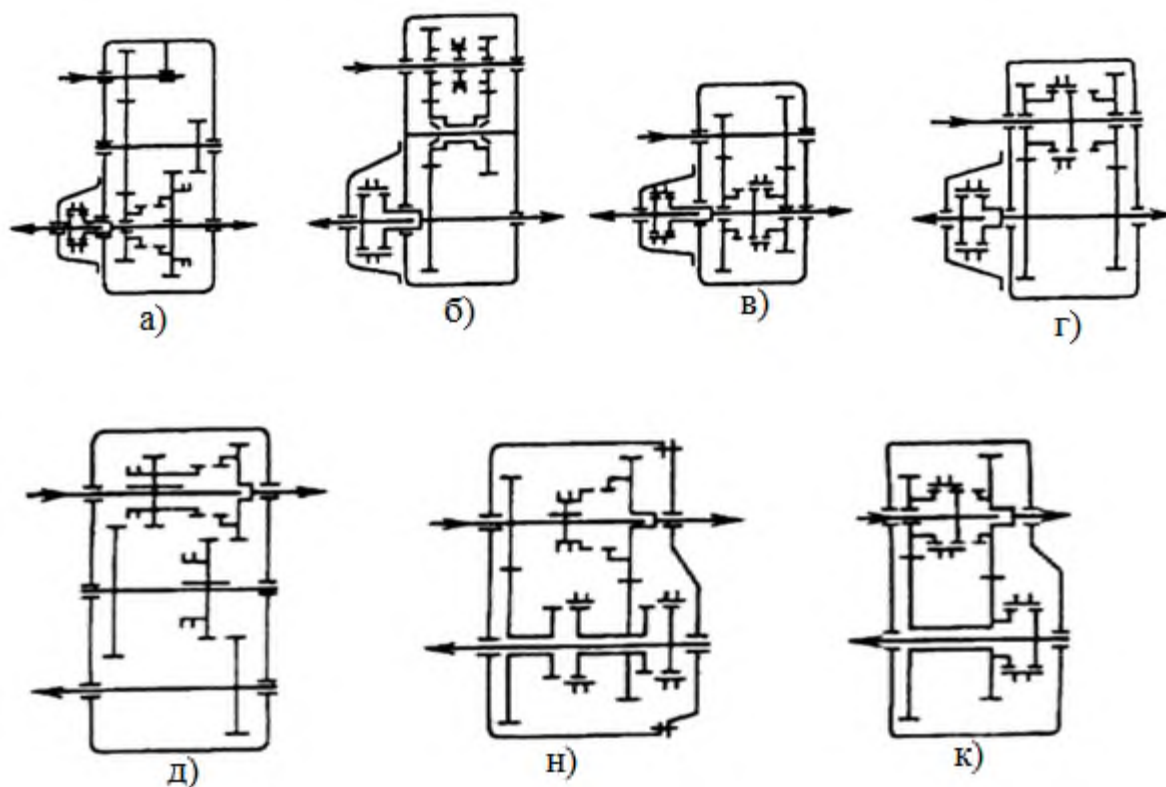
Схемы двухступенчатых раздаточных коробок с заблокированным приводом и соосным(сверху) и несоосными(снизу) ведомыми валами.
